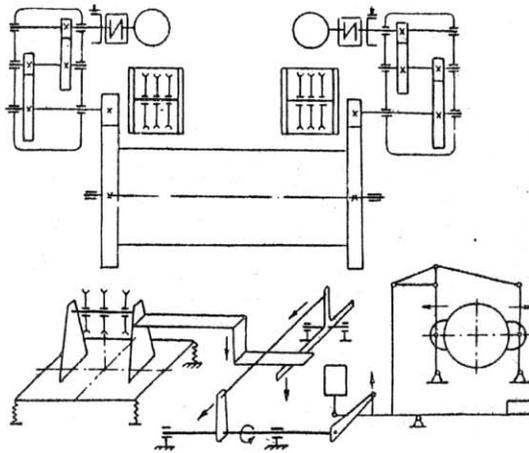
Лебедка с защитой от перегрузок (вариант схемы 13)
